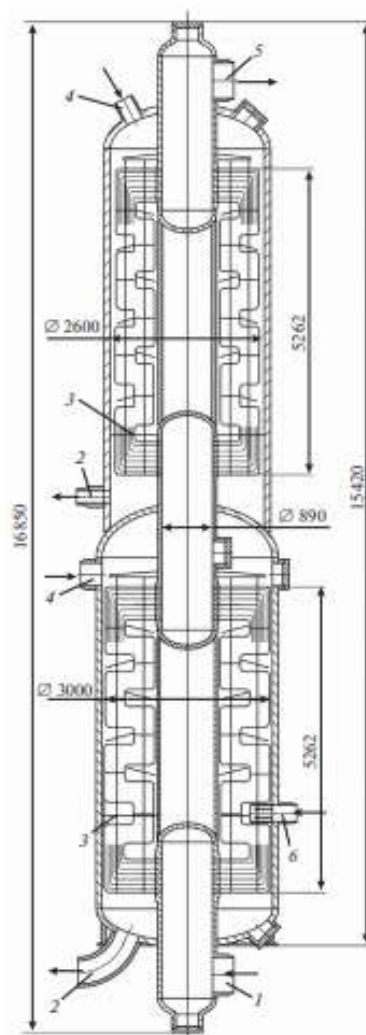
Двойной подогреватель коллекторно-ширмового типа [5]
